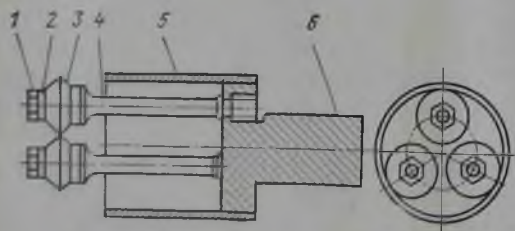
Приспособление для обкатывания конусов буровых штанг:
